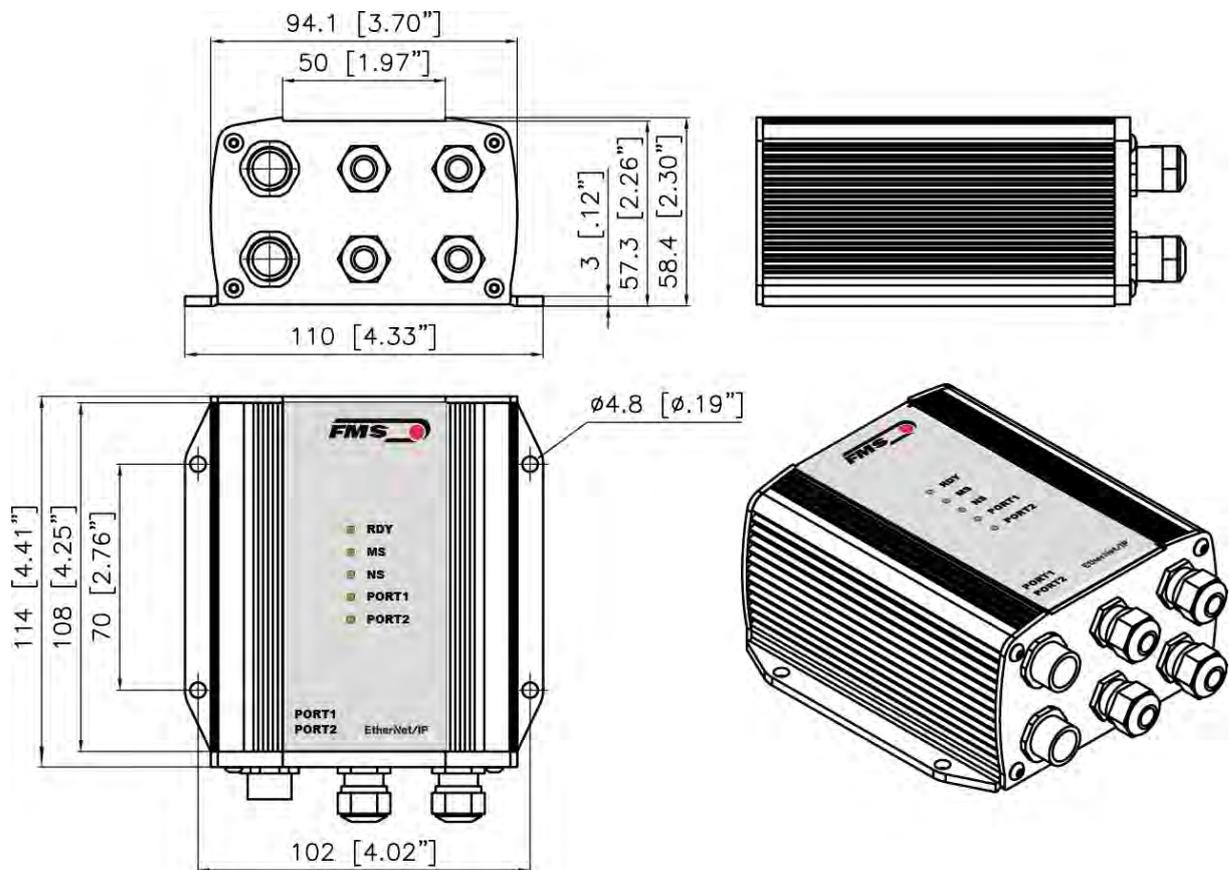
EMGZ492.W.EIP Gehäuse für Wandmontage
